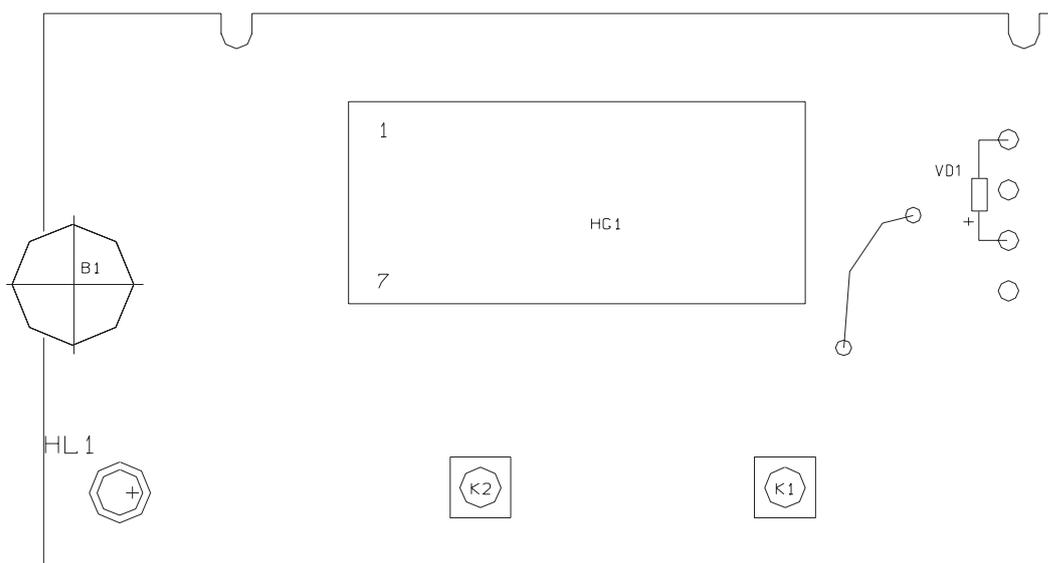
Сборочный чертеж платы обработки ТПГ-94.1. Вариант исполнения 2. Сторона пайки.
